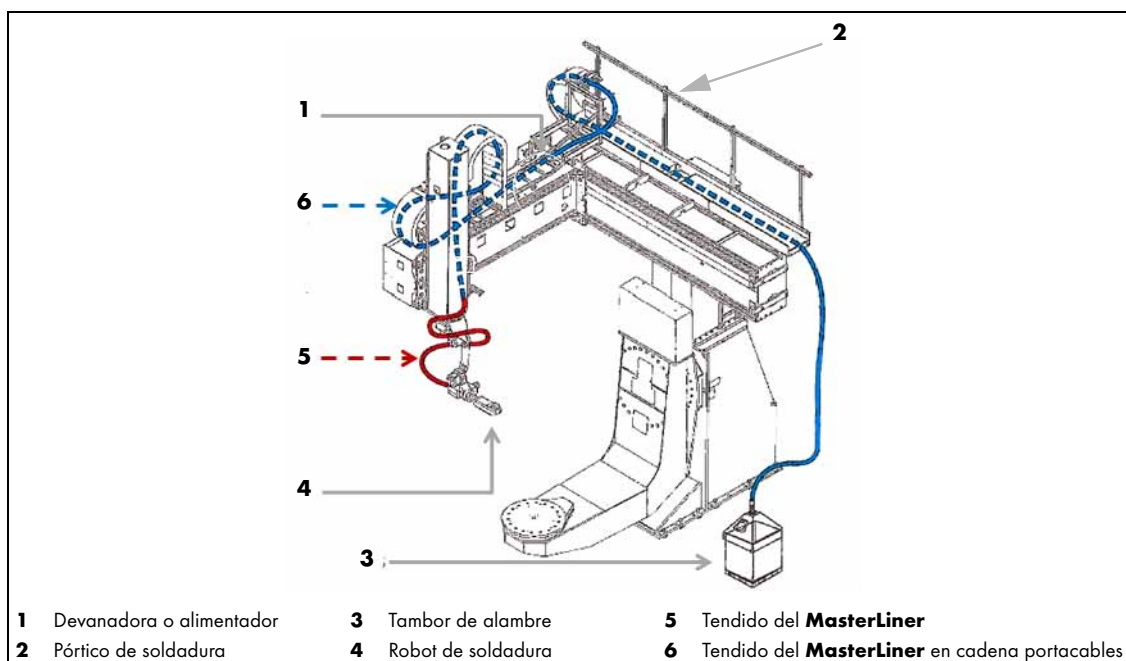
Tendido de la célula de soldadura robotizada
